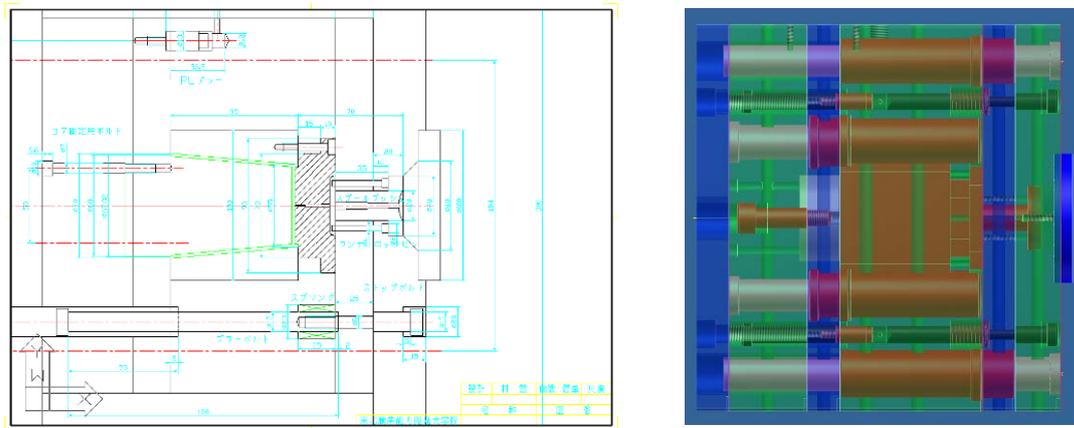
2次元 CAD (左側) と 3次元 CAD (右側)
